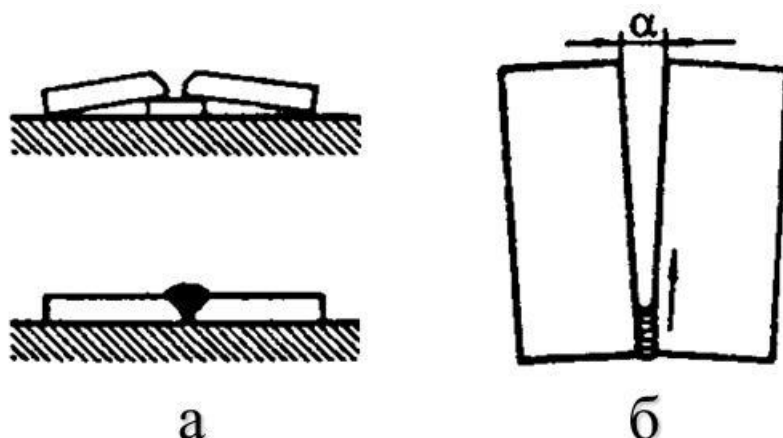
Поздовжня (а) і поперечна (б) ливарна усадка металу шва.
